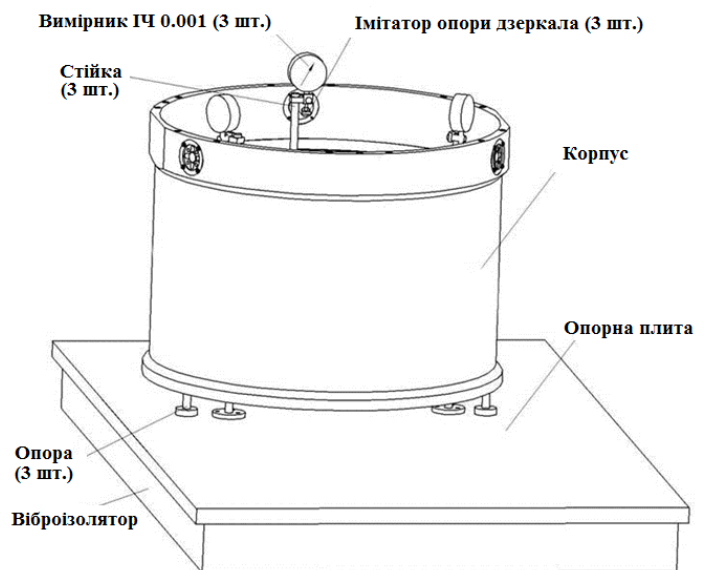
Схема встановлення корпусу та вимірювачів на випробувальній плиті
